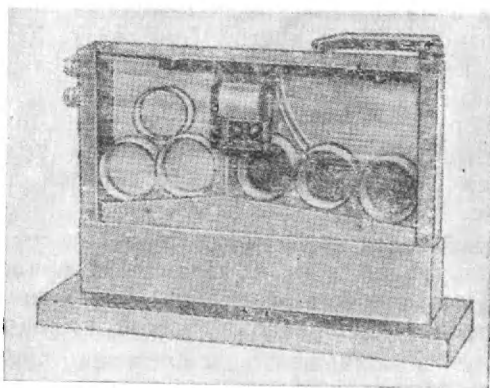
Приставка к фотореле для автоматической сортировки деталей
